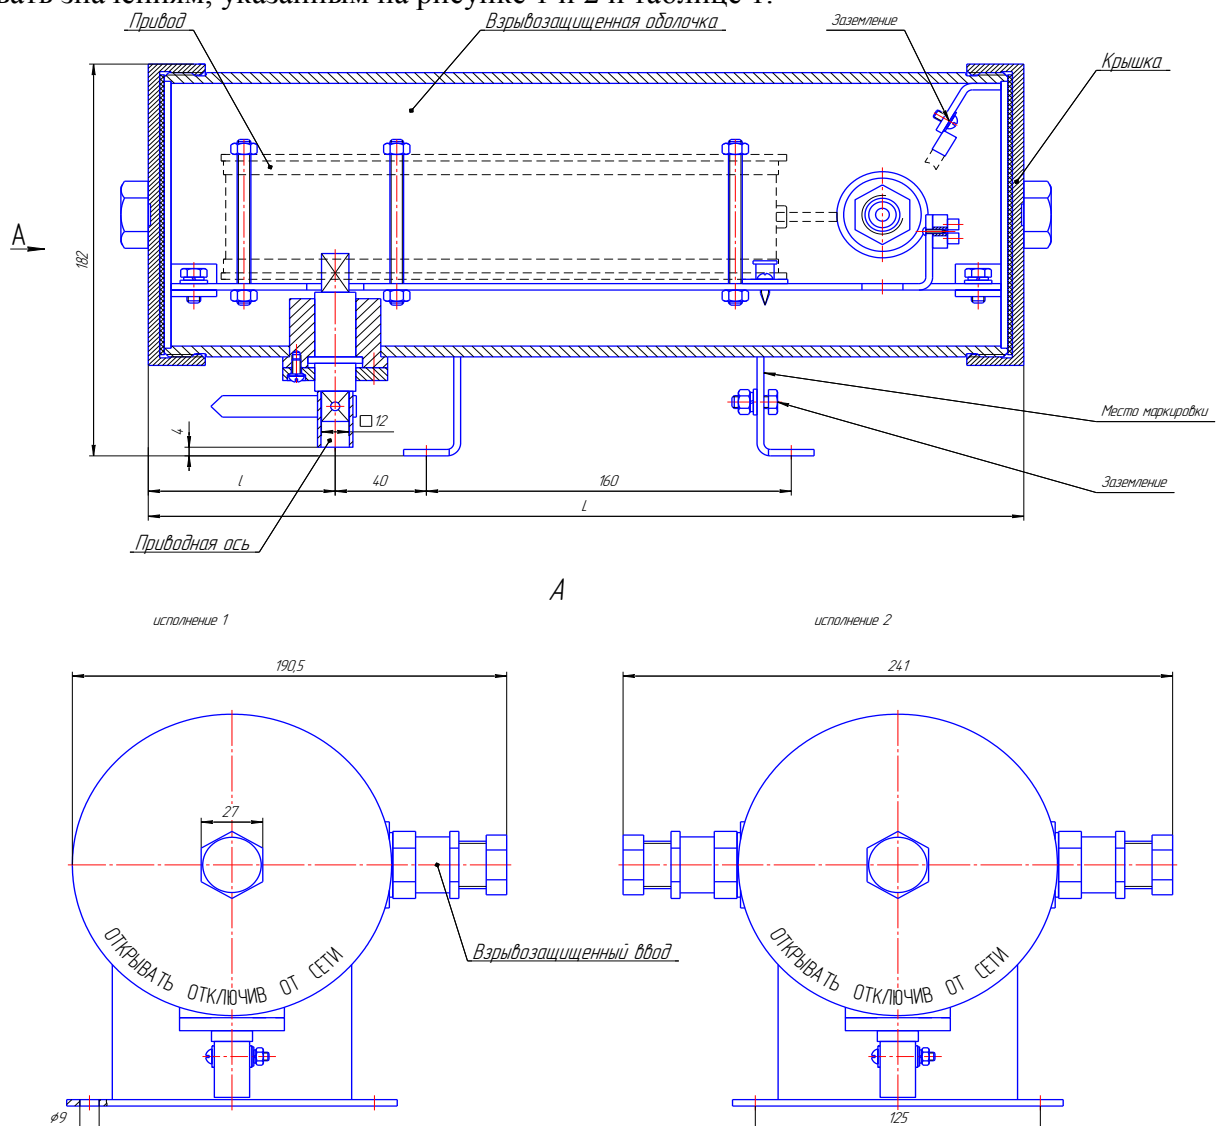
Габаритный чертёж электропривода ЭПВ ВГ 070.00.00.000 с оболочкой из стали
